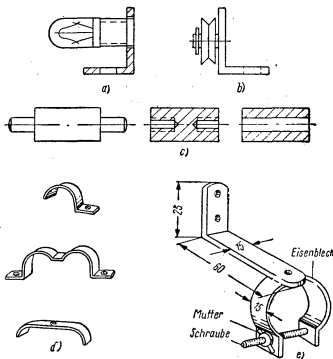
Befestigungsteile; Winkel für Skalenlampe (a), Winkel für Seilrolle (b), Abstandsstücke (c), Befestigungsschellen für Elkos usw. (d) und Halterung für ein magisches Auge (z. B. 6 E 5) (e)
